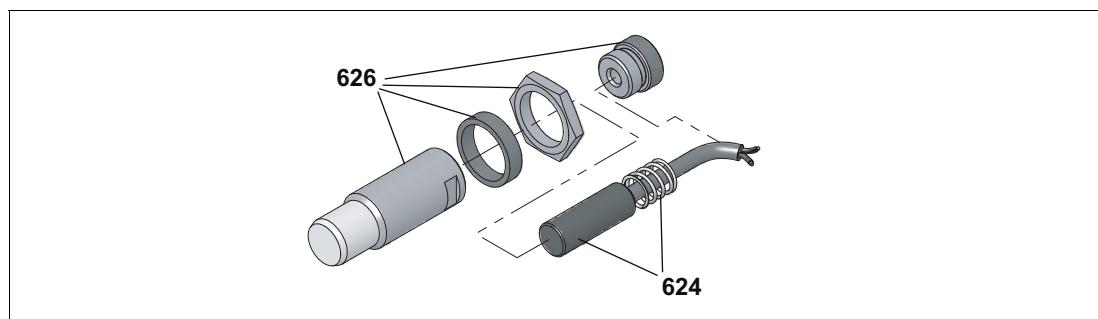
Explosionszeichnung BEG 47D/BEG 47E/BEG 47G
